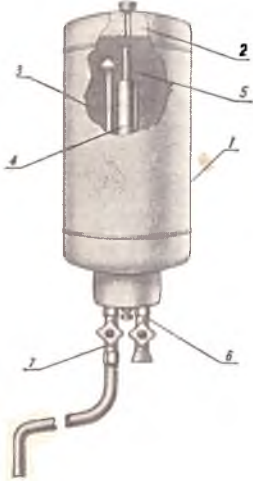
Бойлер электрический кухонный настенный вертикальный: 1 — кожух (наружный корпус); 2 — теплоизоляция; 3 — резервуар для воды; 4 — нагревательный элемент; 5 — стержень терморегулятора (термодатчик); 6 — впускная труба с краном; 7 — труба с краном для выпуска горячей воды
